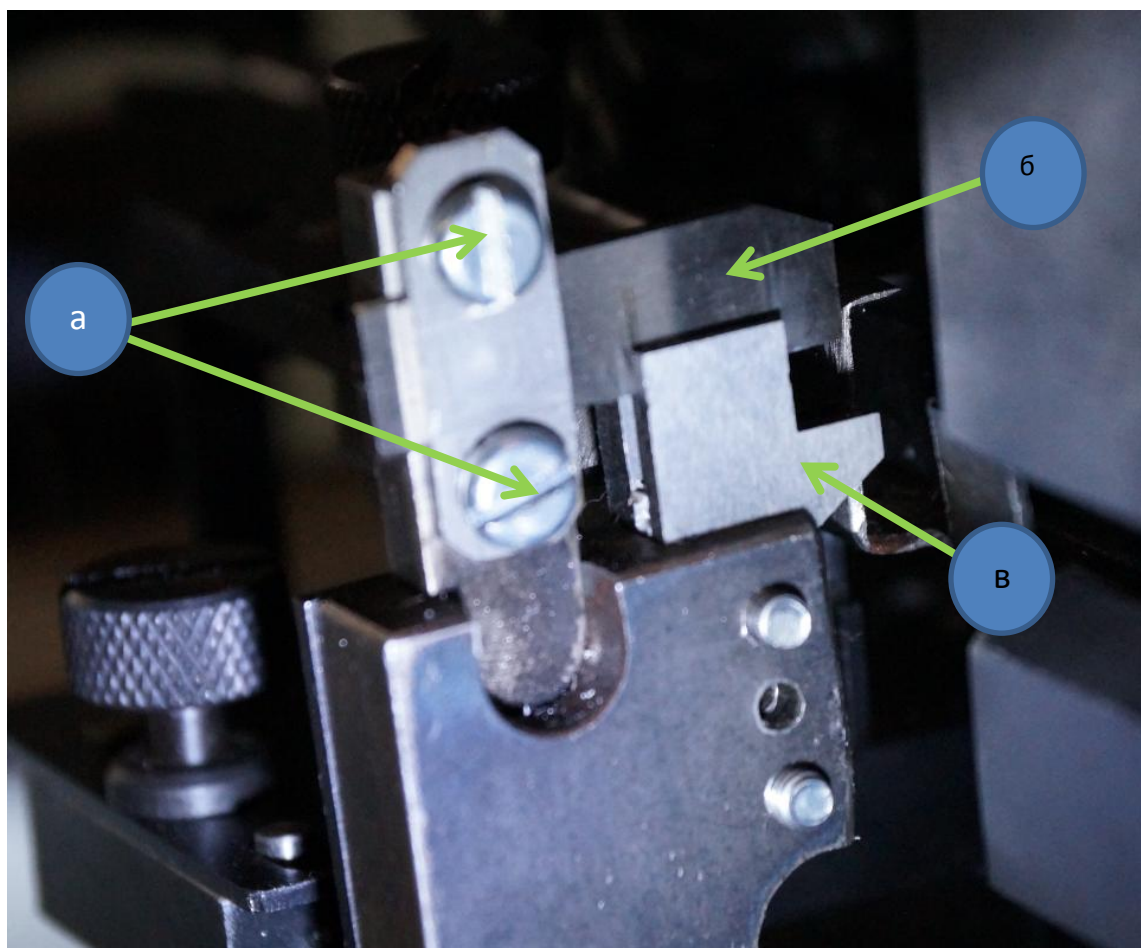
Нож и противоножи устройства реза. Нож показан в верхнем положении. А-винты планки крепления верхнего ножа, б- верхний нож, в- противоножи.
